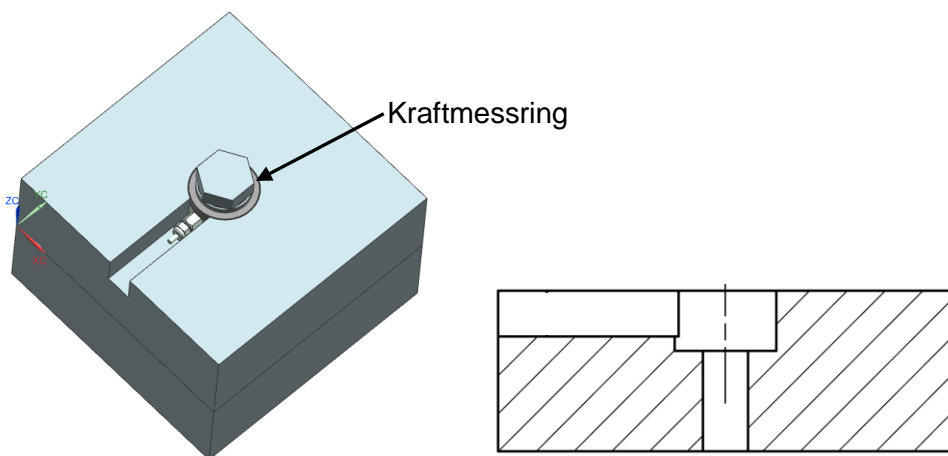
Versuchsaufbau mit Kraftmessring und Schnittansicht durch oberes Blech (Bohrungen und Fräsungen für Kraftmessring)
